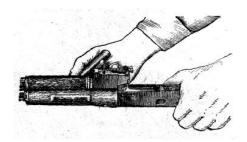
Поворот замыкателя газовой трубки с помощью пенала принадлежности
